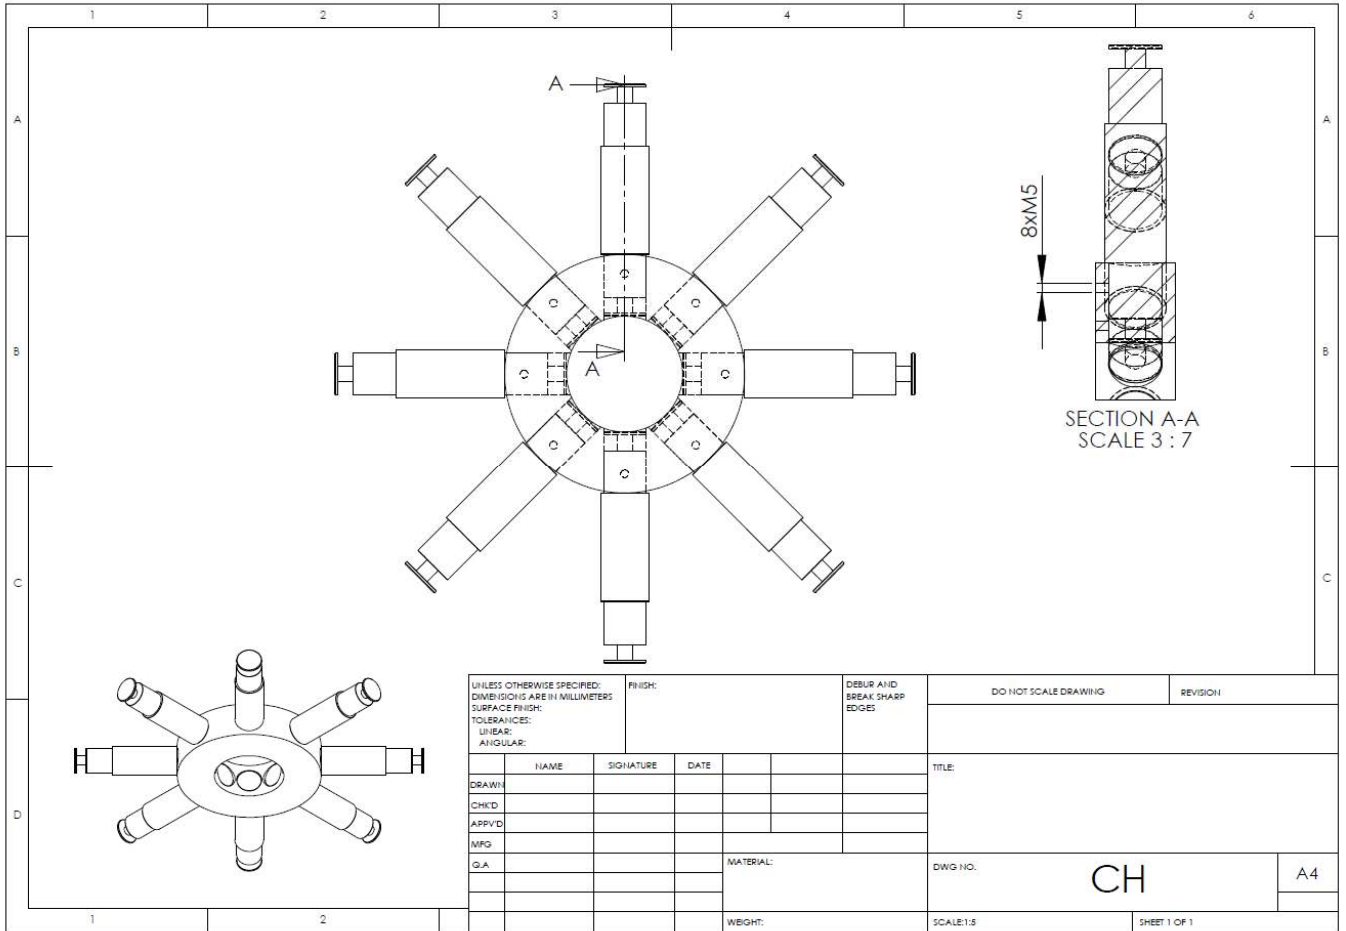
Desenho técnico conjunto do sistema BAC Circular.
